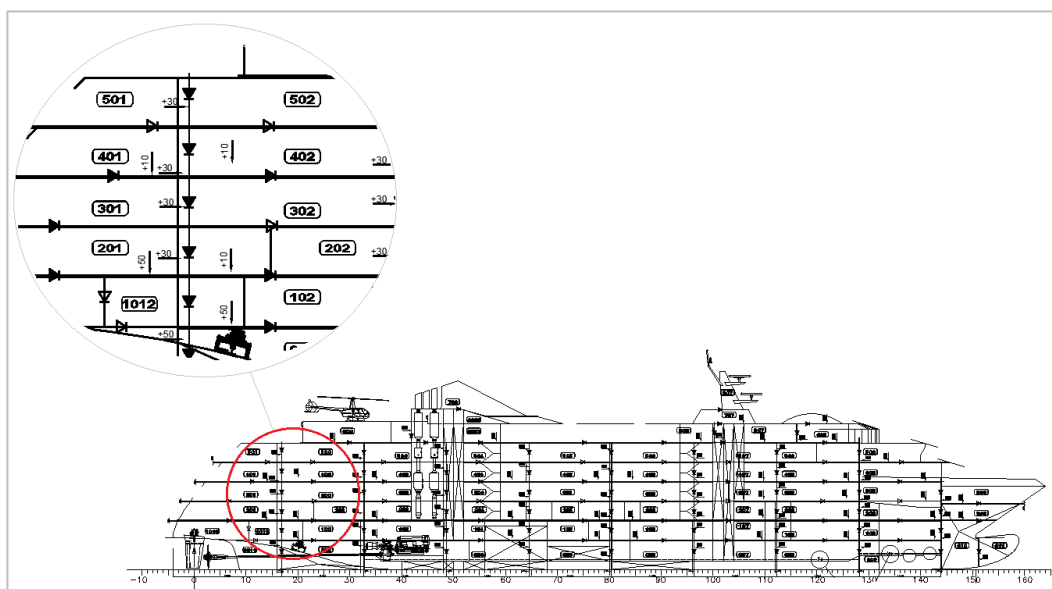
Estratégia de montagem e soldadura de blocos (Fonte: West-sea)
